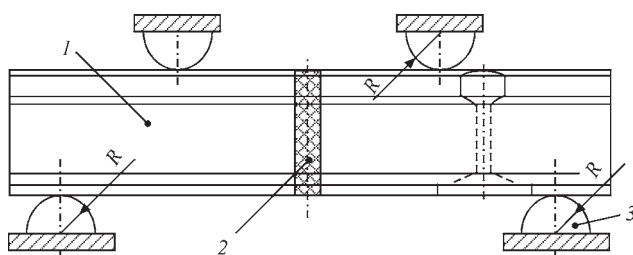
Випробування зварного з'єднання на міцність від утоми: 1 – вид збоку; 2 – зварний шов; 3 – опора
